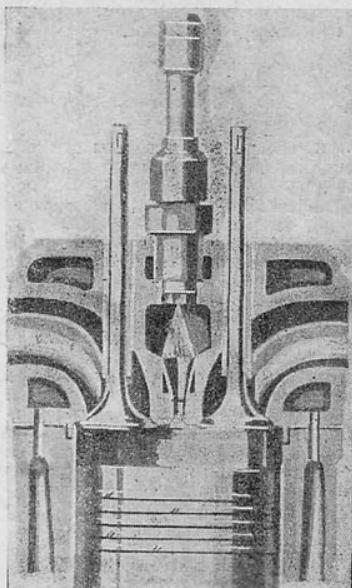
Форкамера тихоходного лодочного дизель-мотора
